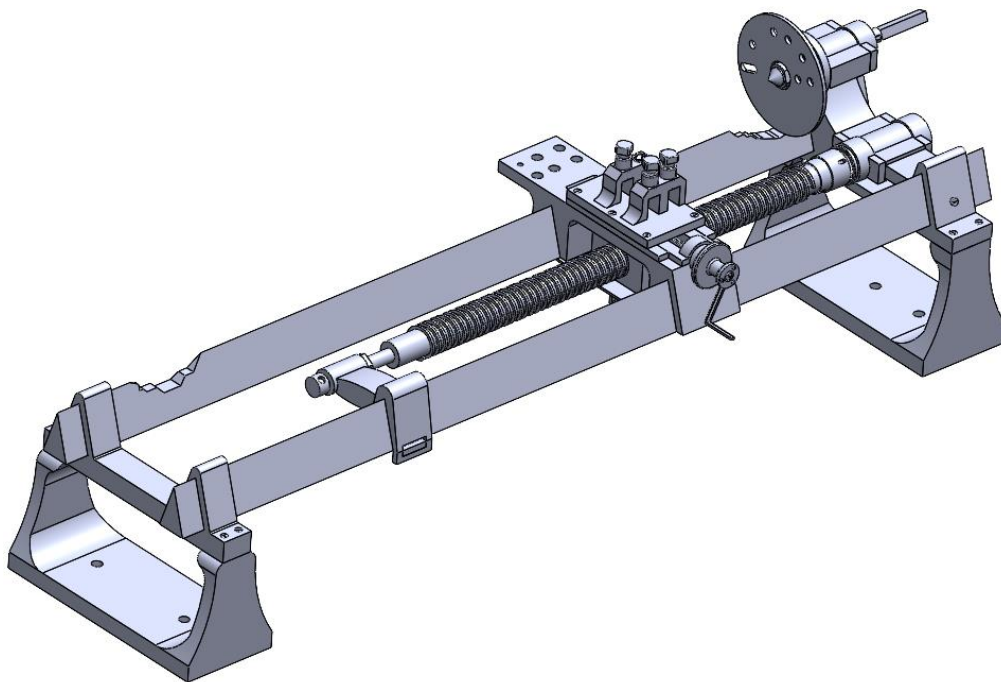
Carro longitudinal ensamblado en el cuerpo del torno.
